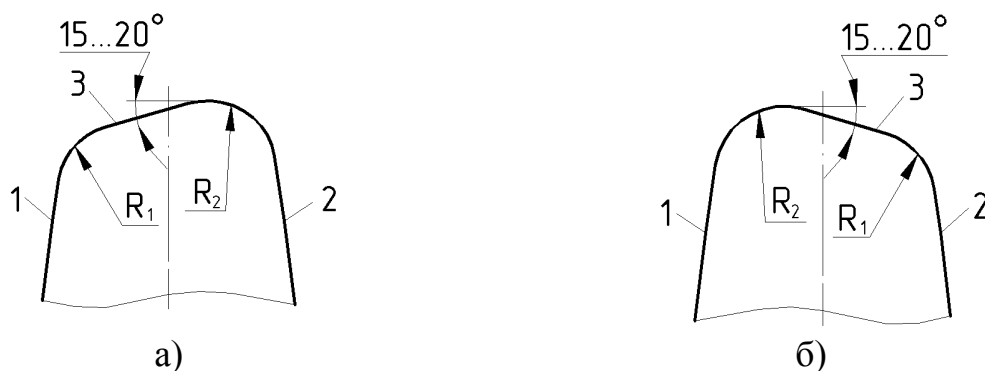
Профили режущих кромок зубьев червячной фрезы с наклоном вершинных режущих кромок зуба: а – нечетных зубьев; б – четных зубьев
